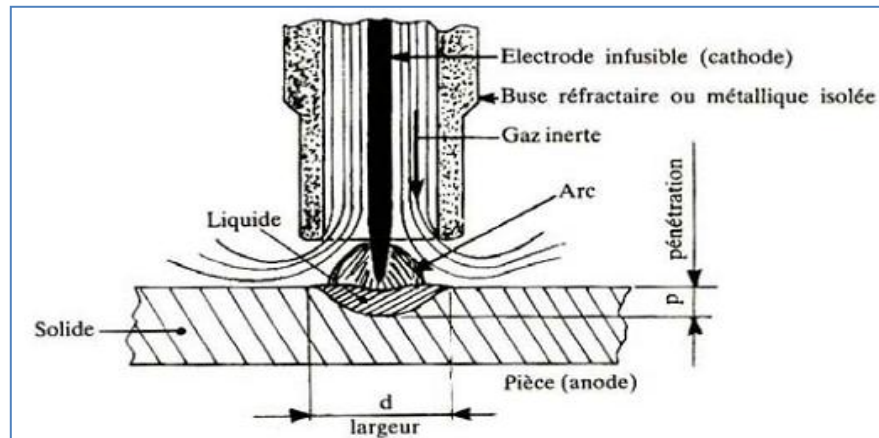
Principe du procédé de soudage TIG simple flux. [8]
